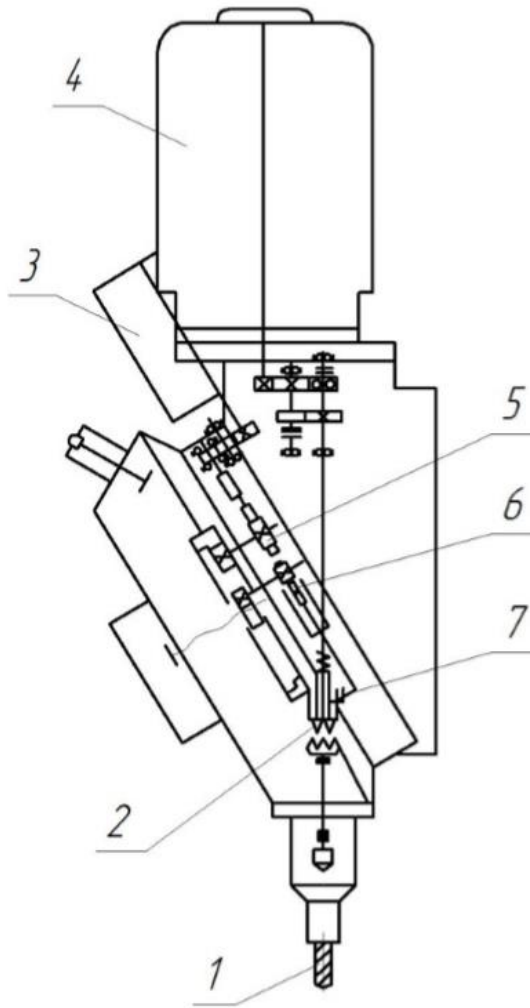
Конструкція привода з револьверною головою з поворотними шпинделями
